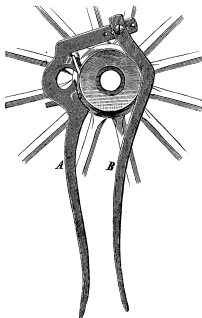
Werkzeug zum Anlegen der Nabenreifen.
